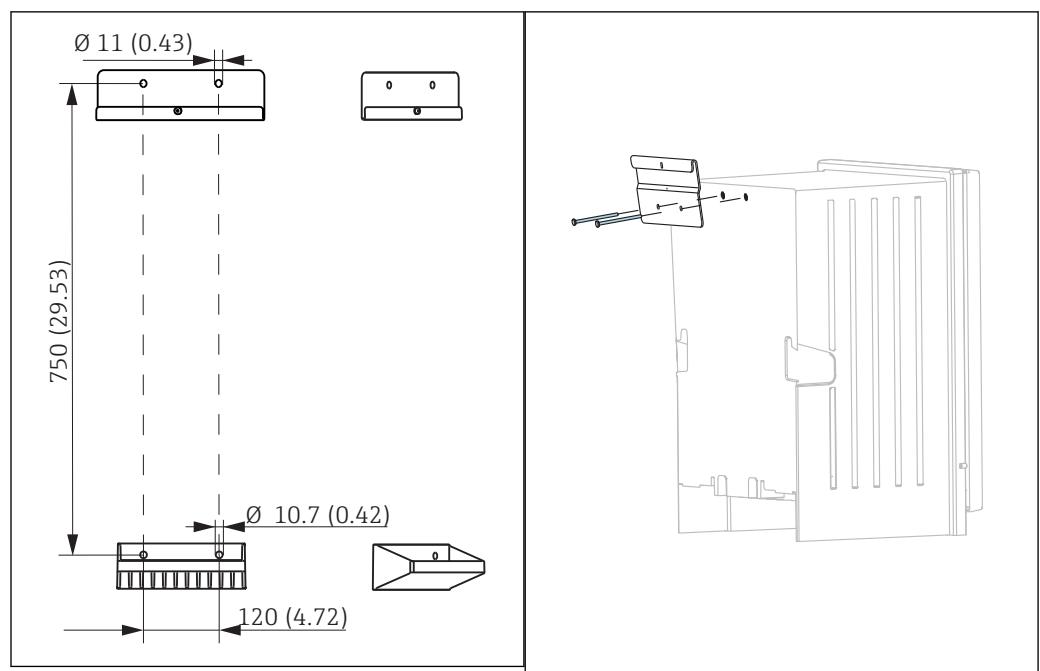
支架的外形尺寸示意图; 单位: mm (inch)
